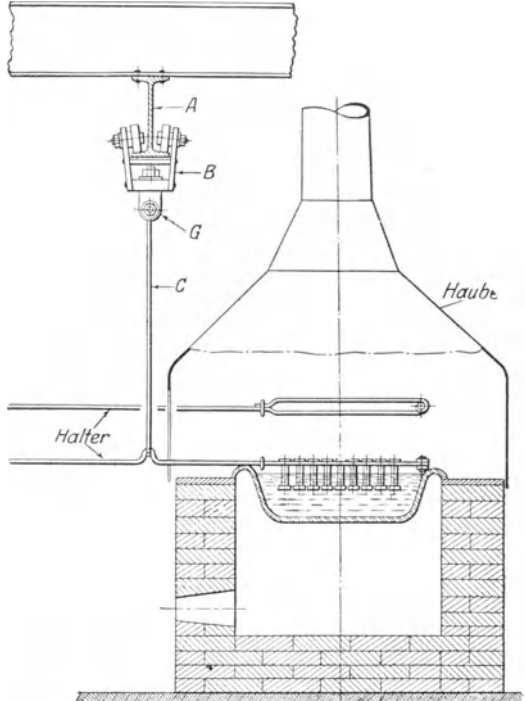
Beförderungseinrichtung für Badöfen. A Träger, B Laufkatze, C Schwenkarm, G Gelenk.
